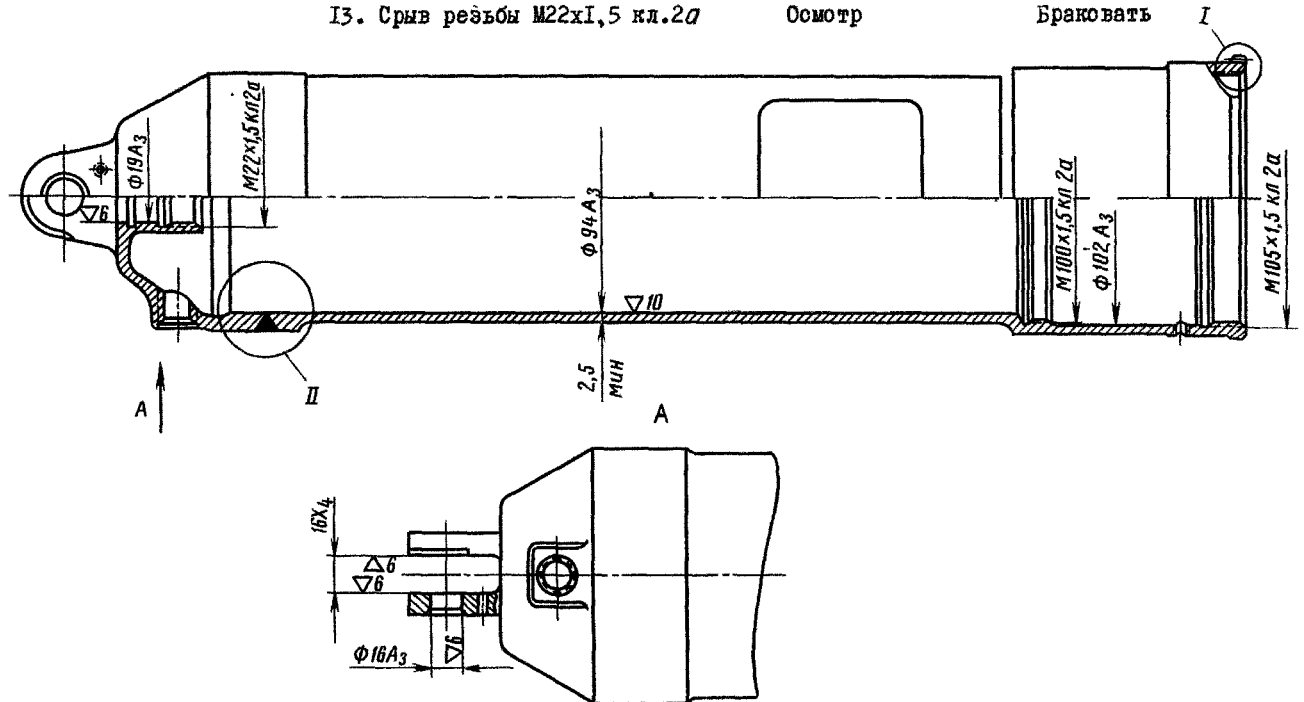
Цилиндр в сборе 8А-4101-100-А
